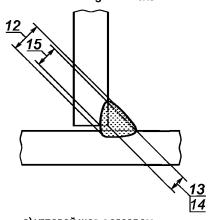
Толщины угловых швов Figure 14 — Throat thicknesses for fillet welds Figure 14 — Gorges des soudures d'angle
